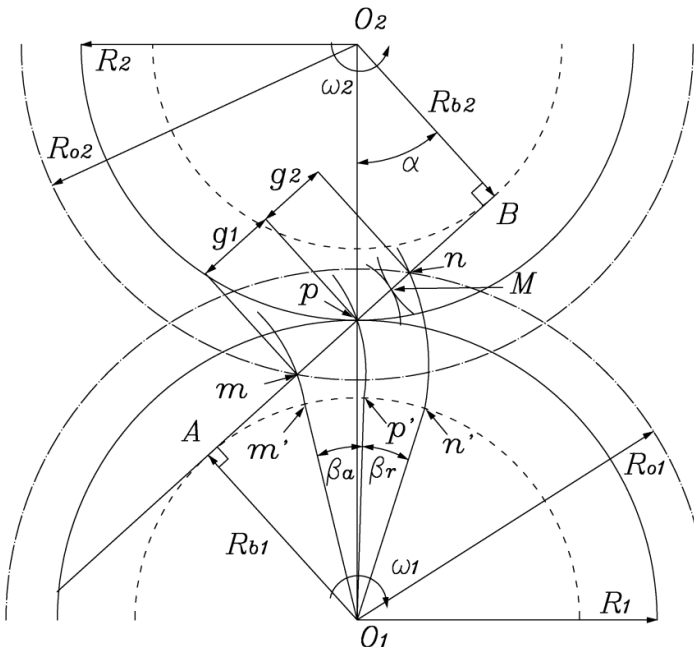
Relações geométricas das engrenagens externas de dentes retos
